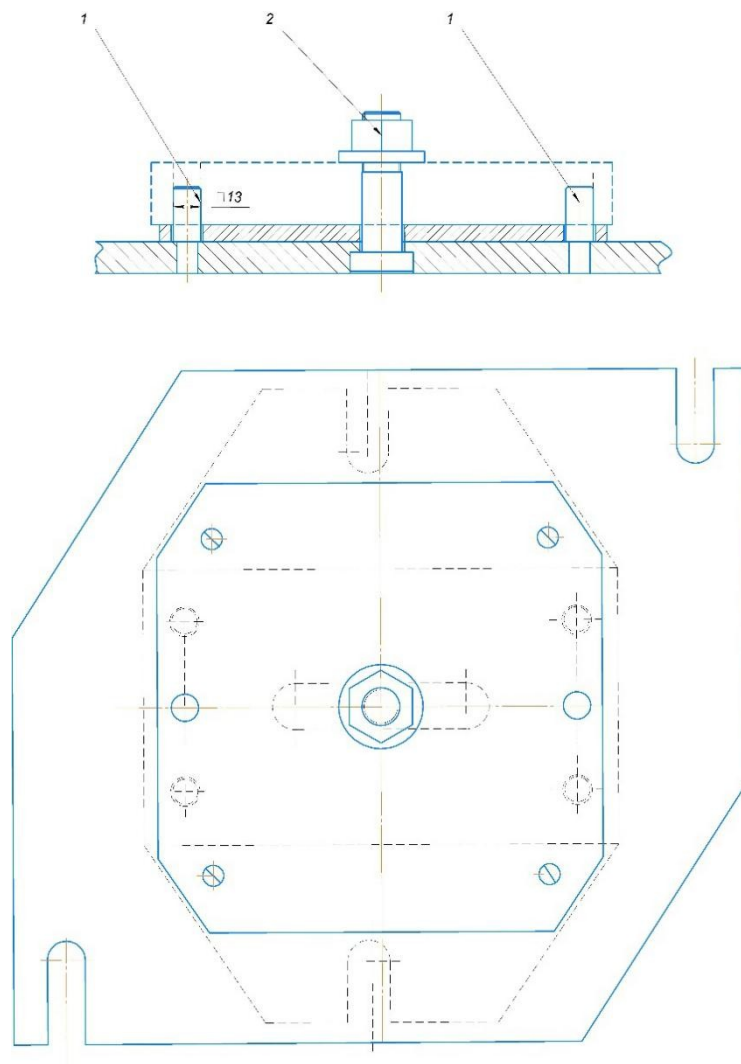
Загальне креслення верстатного пристрою на фрезерний верстаті з ЧПУ HAAS VF-2
